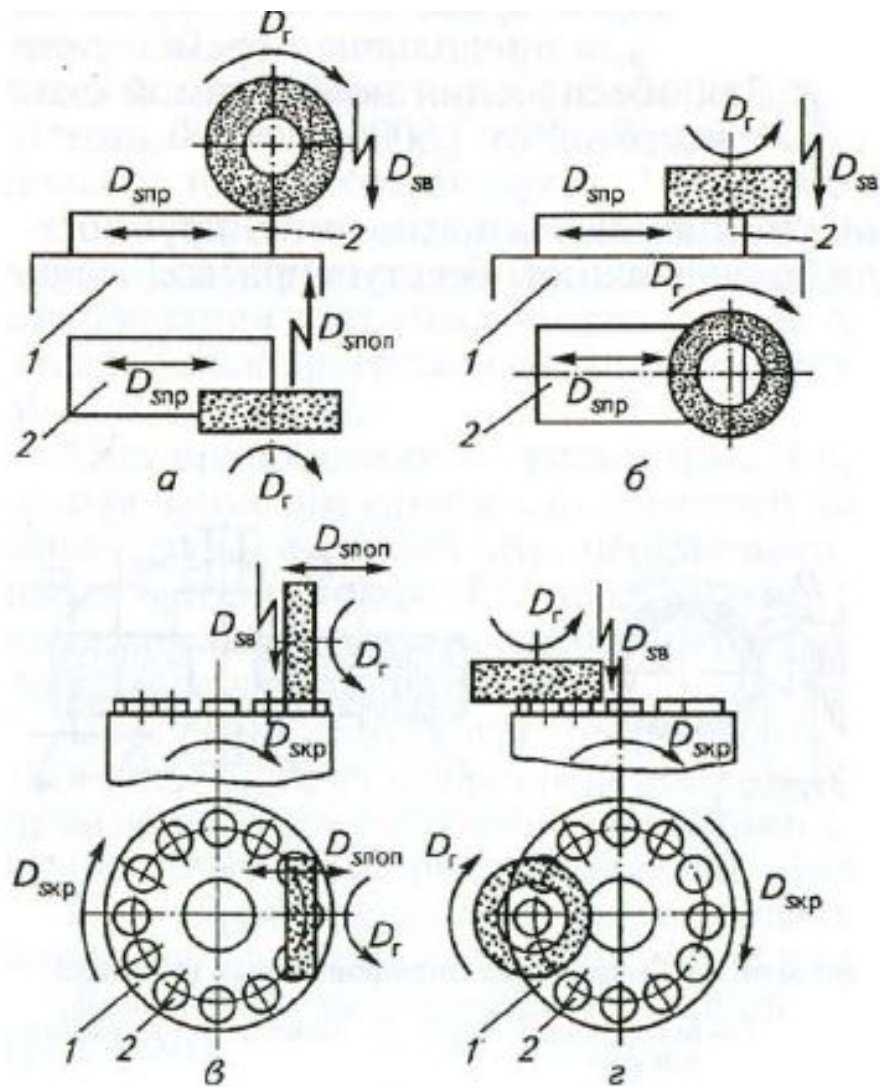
Схемы обработки заготовок на плоскошлифовальных станках:
